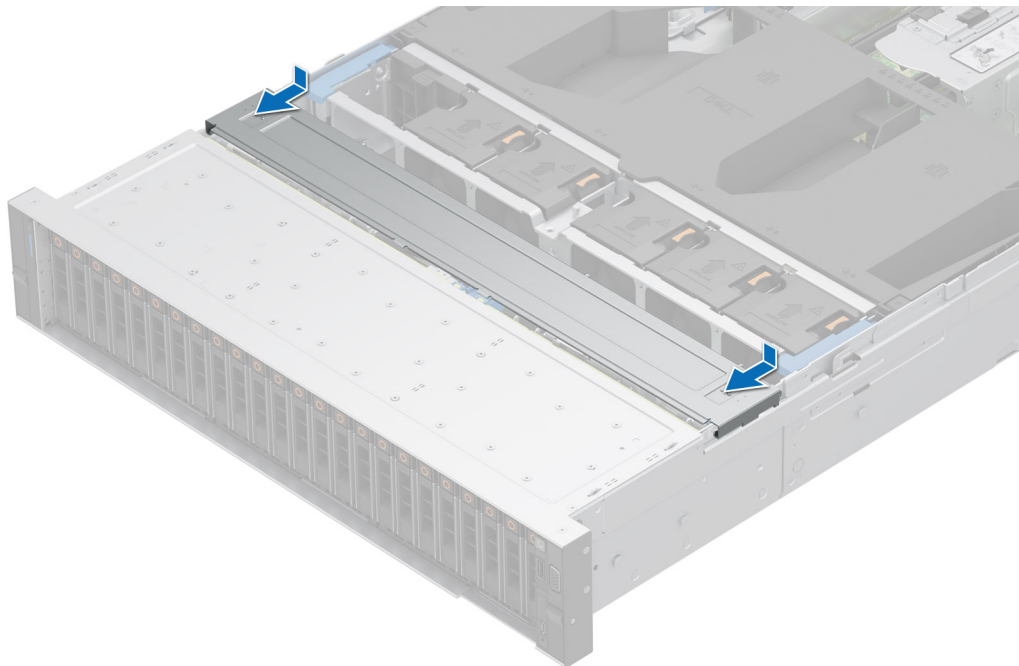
Extracción de la cubierta del backplane de la unidad
